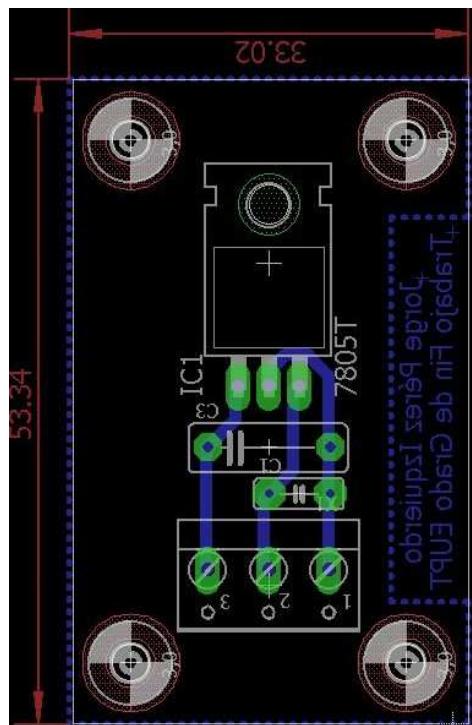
Pistas, componentes y planos de masa de la placa del regulador.
